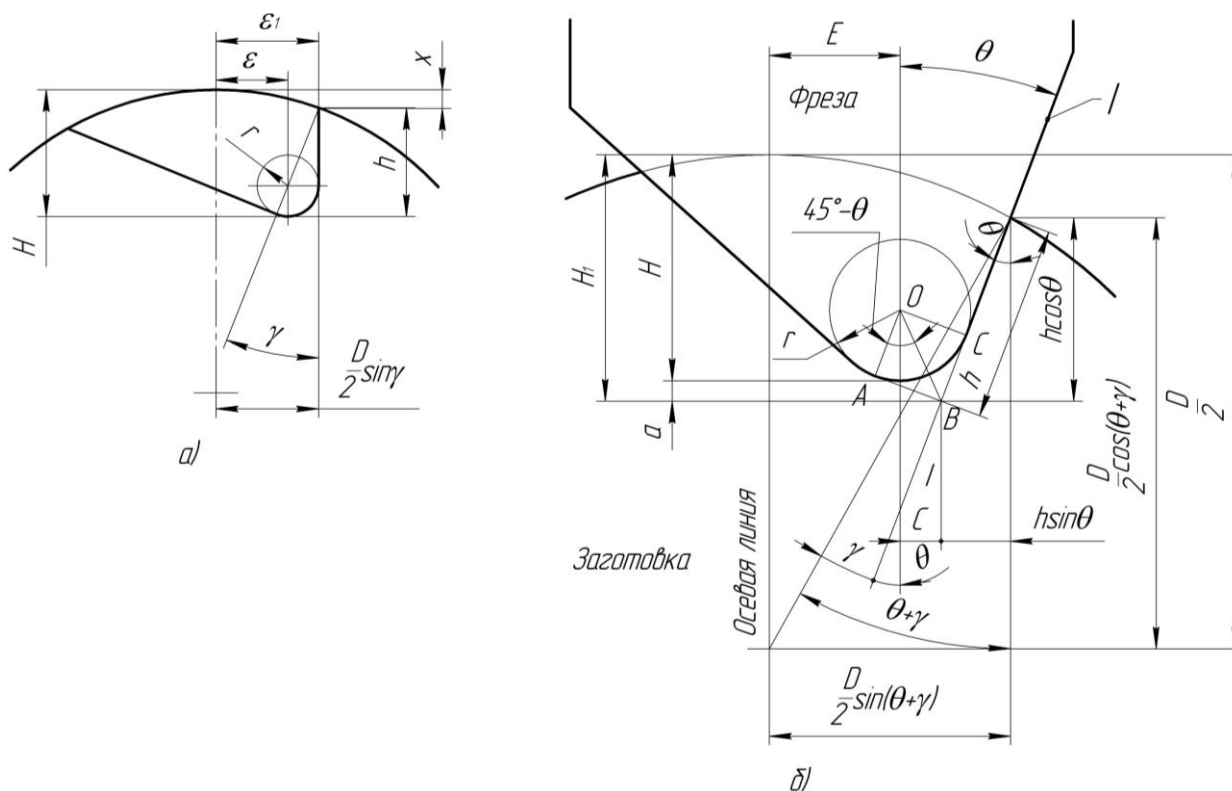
Схемы: *a* — расчета при фрезеровании прямых зубьев одноугловой фрезой; *б* — фрезерования прямых зубьев двухугловой фрезой
